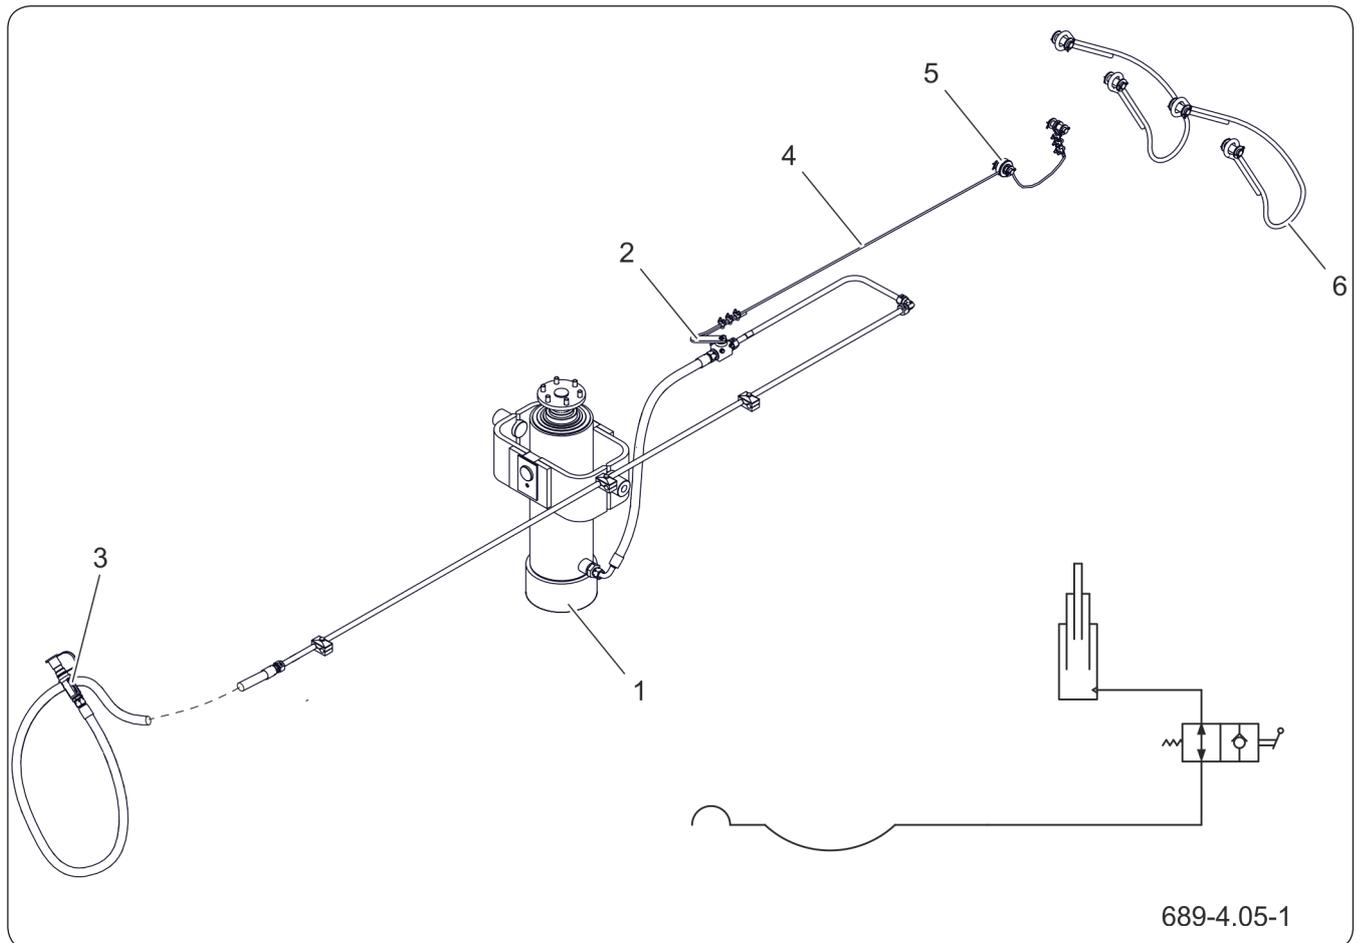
Construction et schéma de l'installation hydraulique du dispositif de basculement
